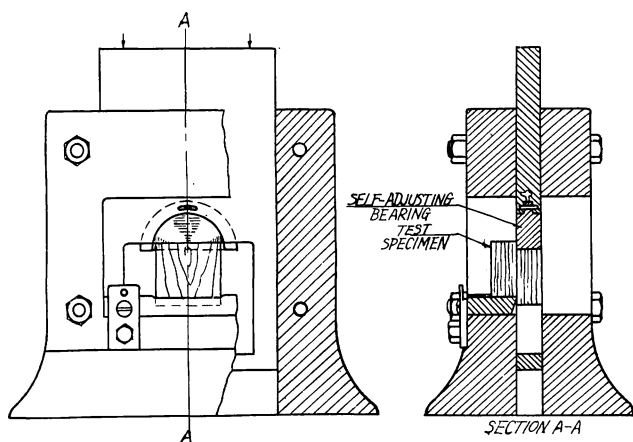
F. P. L. 剪断型接着力試験片用特殊剪断装置
